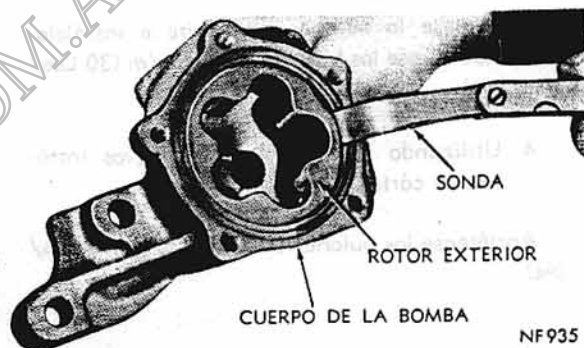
Medición de la Tolerancia del Rotor Exterior.
